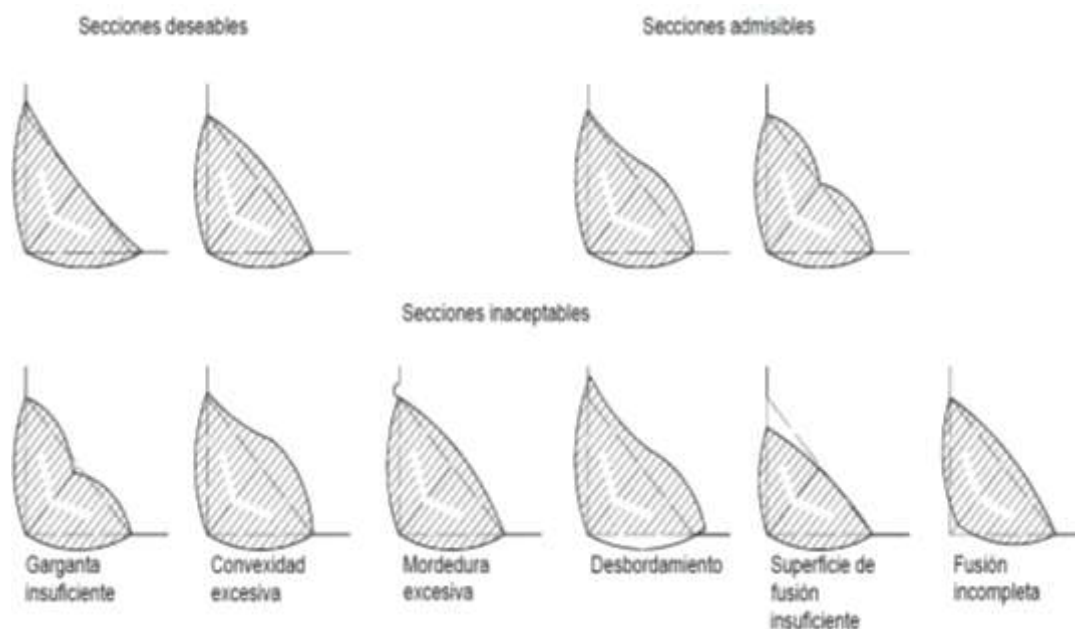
Defectos de Forma en Soldaduras de Angulo
